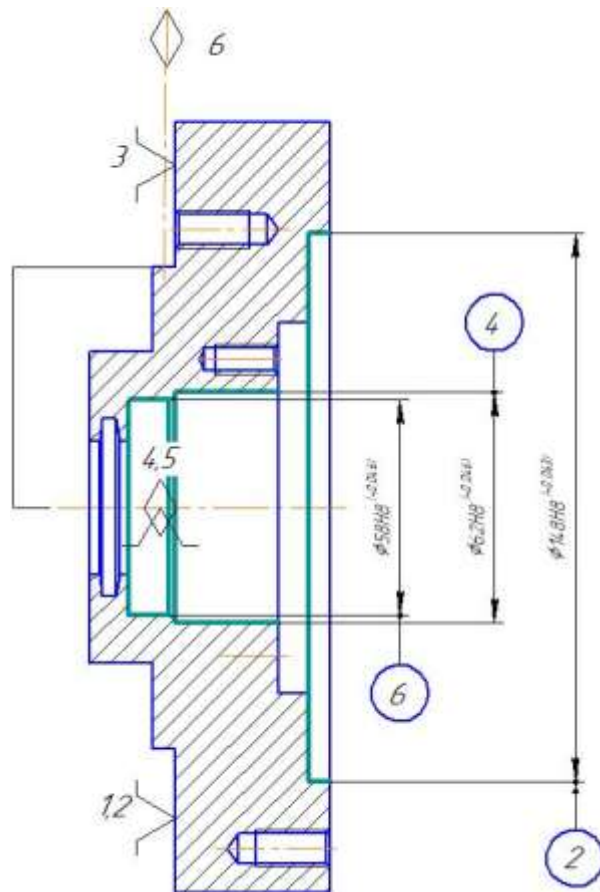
Ескіз механічної обробки із схемою базування (операція 025)
